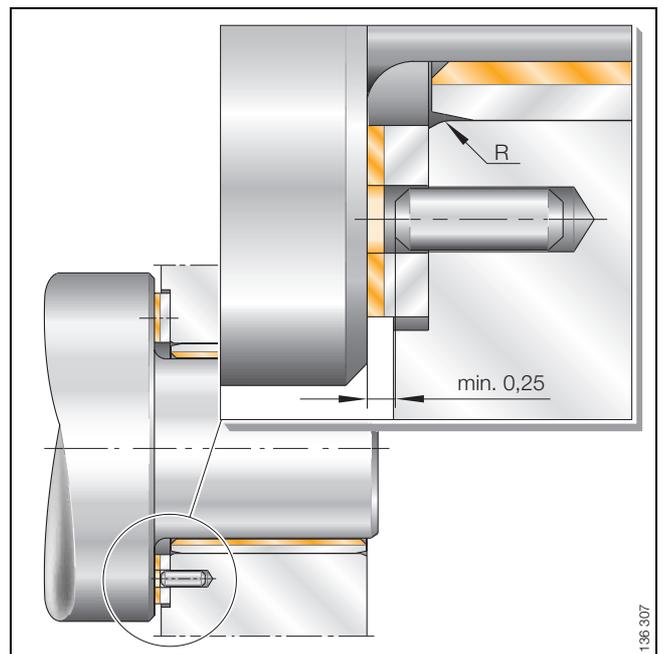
· Befestigen einer Anlaufscheibe PAW in einer Ausnehmung des Gehäuses
